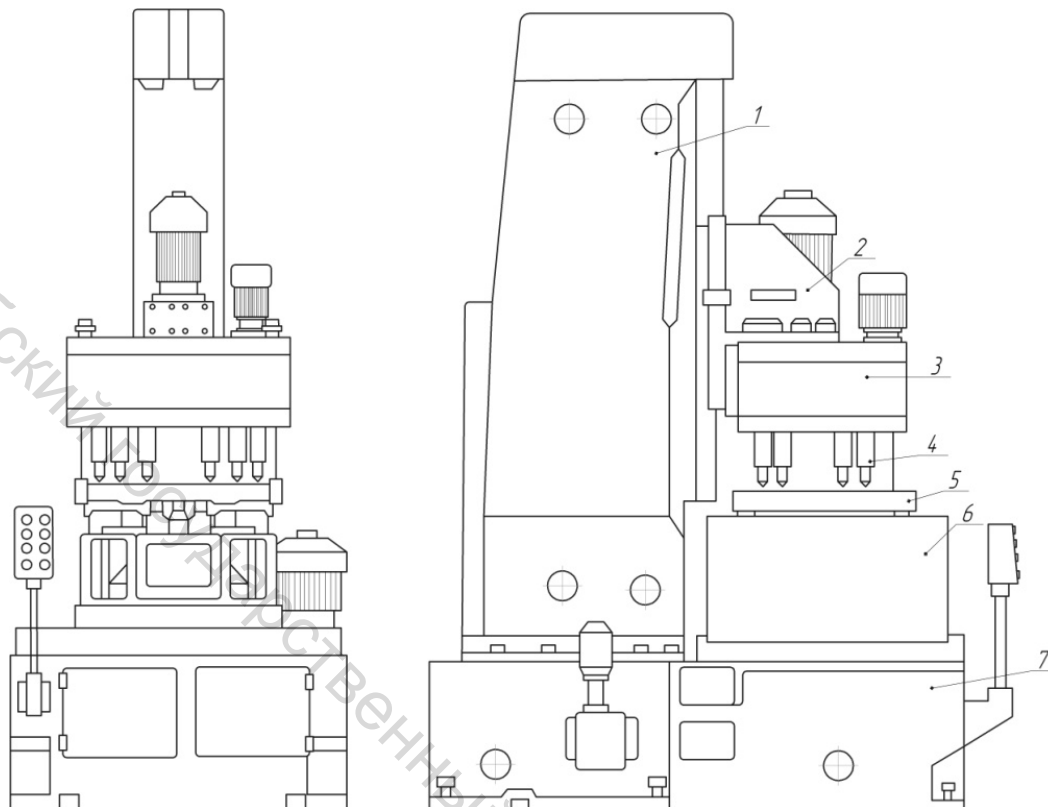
24-шпиндельный вертикальный сверлильно-резьбонарезной агрегатный станок: 1 – вертикальная стойка станины; 2 – силовая головка; 3 – шпиндельная коробка; 4 – инструмент; 5 – кондукторная плита; 6 – приспособление; 7 – основание (базовая плита станины)
